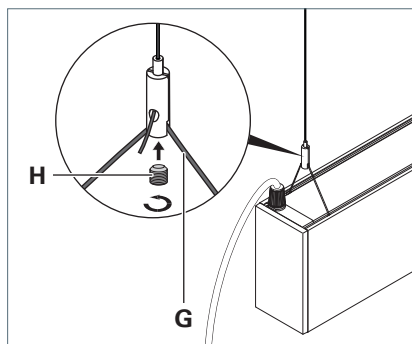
Fissaggio dell'apparecchio al fermacavo.
